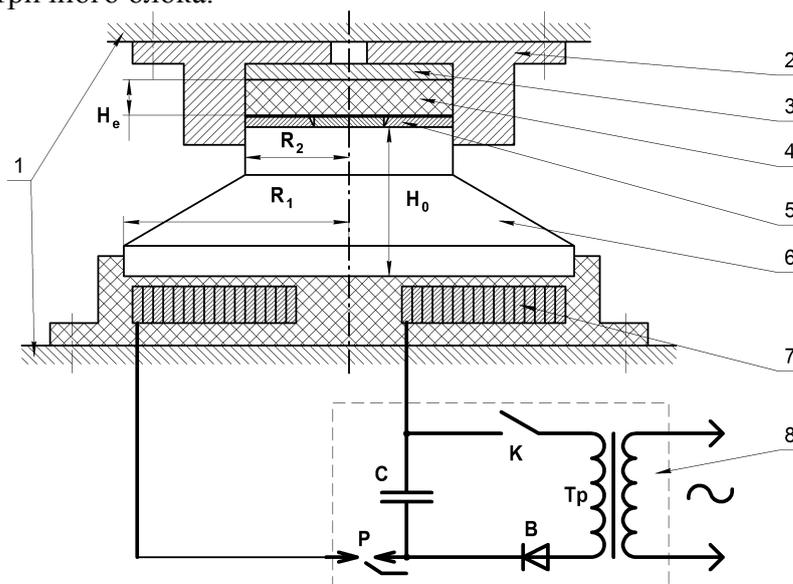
Схемы технологического устройства для МЭИШ и МИУ: 1 – верхняя и нижняя плиты механического прижима, 2 – контейнер, 3 – подкладная плита, 4 – полиуретан, 5 – матричный блок с заготовкой из тонколистового металла, 6 – ступенчатый подвижный элемент, 7 – плоский спиральный индуктор, 8 – блок магнитно-импульсной установки
